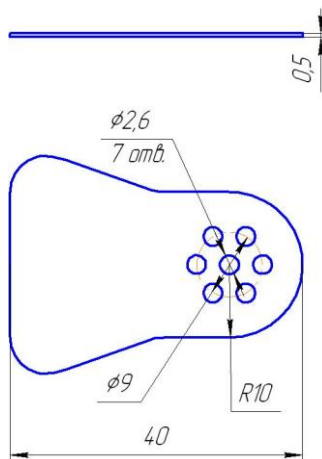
Размеры и форма заготовки при формовке детали «скоба».
